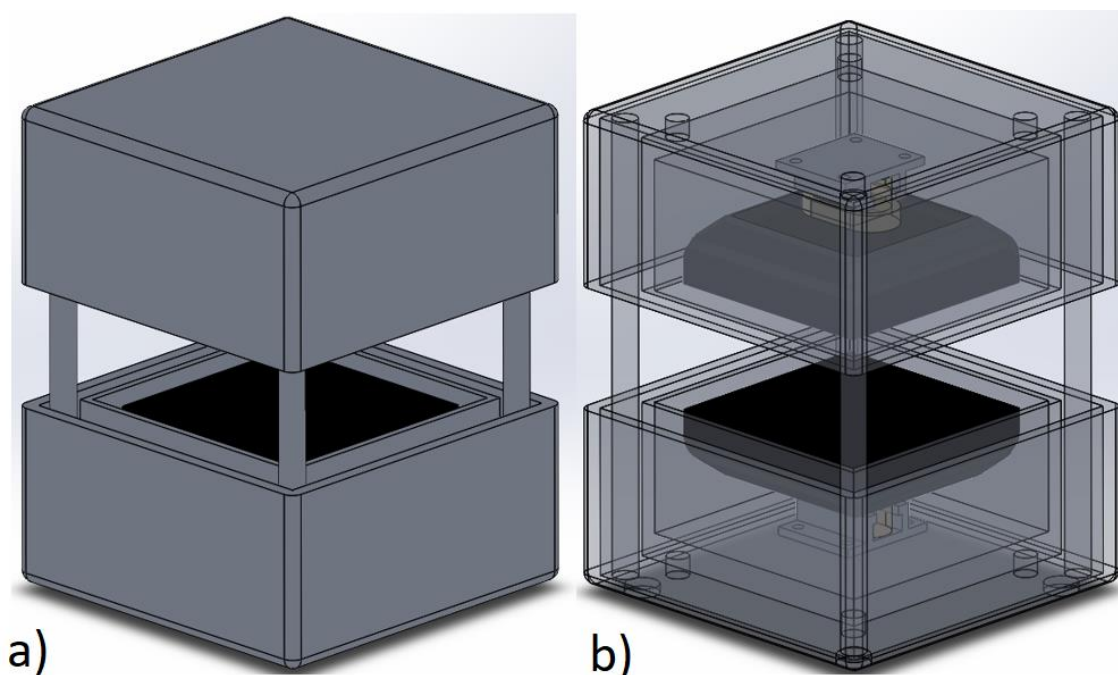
CAD model – Hliníkový chladič (tzv. *heat sink*)
